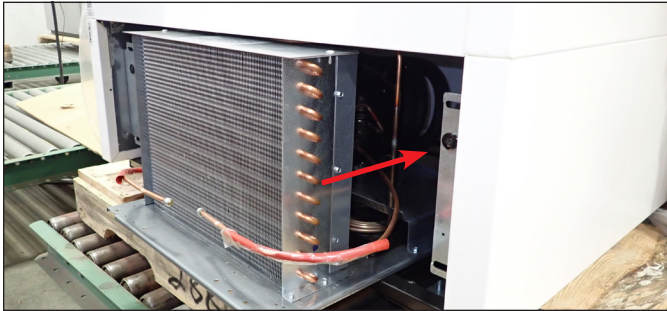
Die Schrauben des Verflüssigersockels entfernen.
